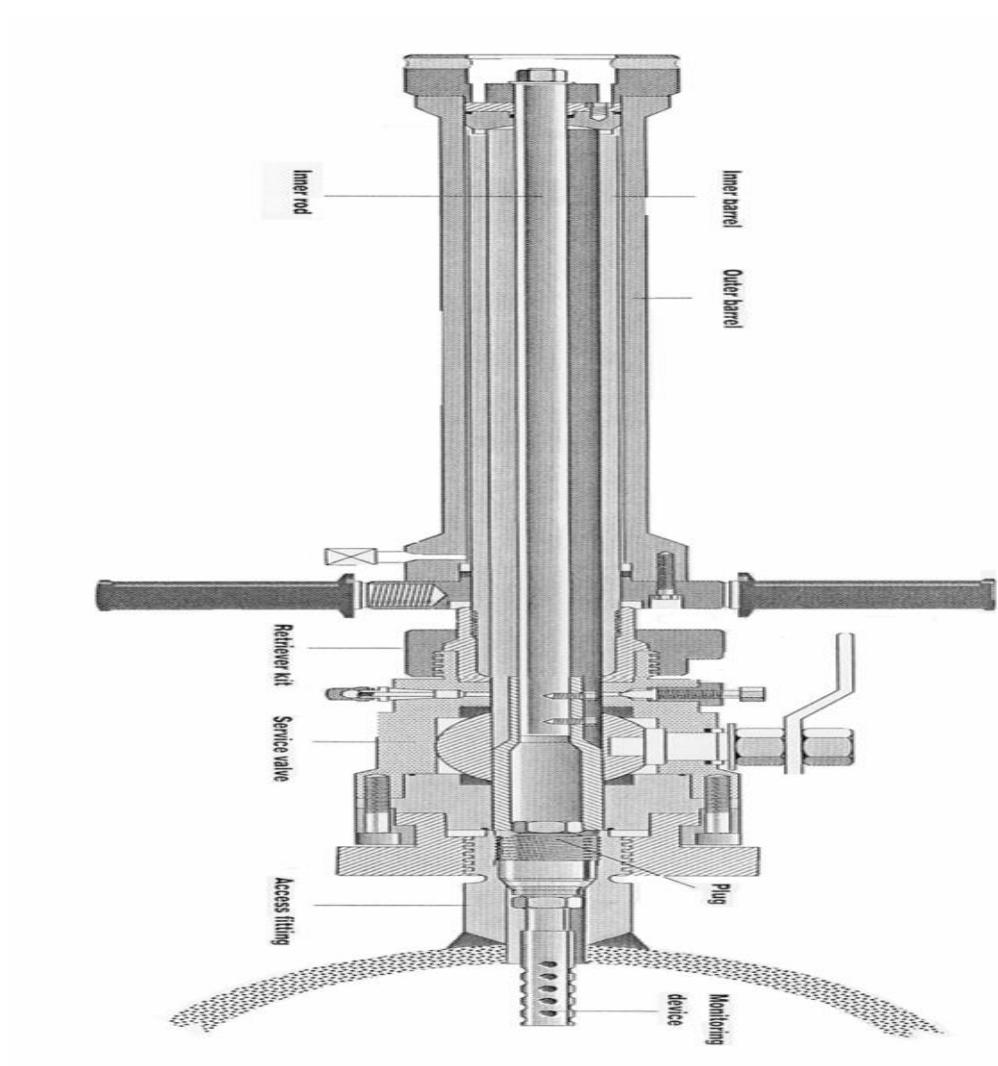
Сборочной чертеж типичного устройства установки – извлечения датчиков через 2" узел ввода.
